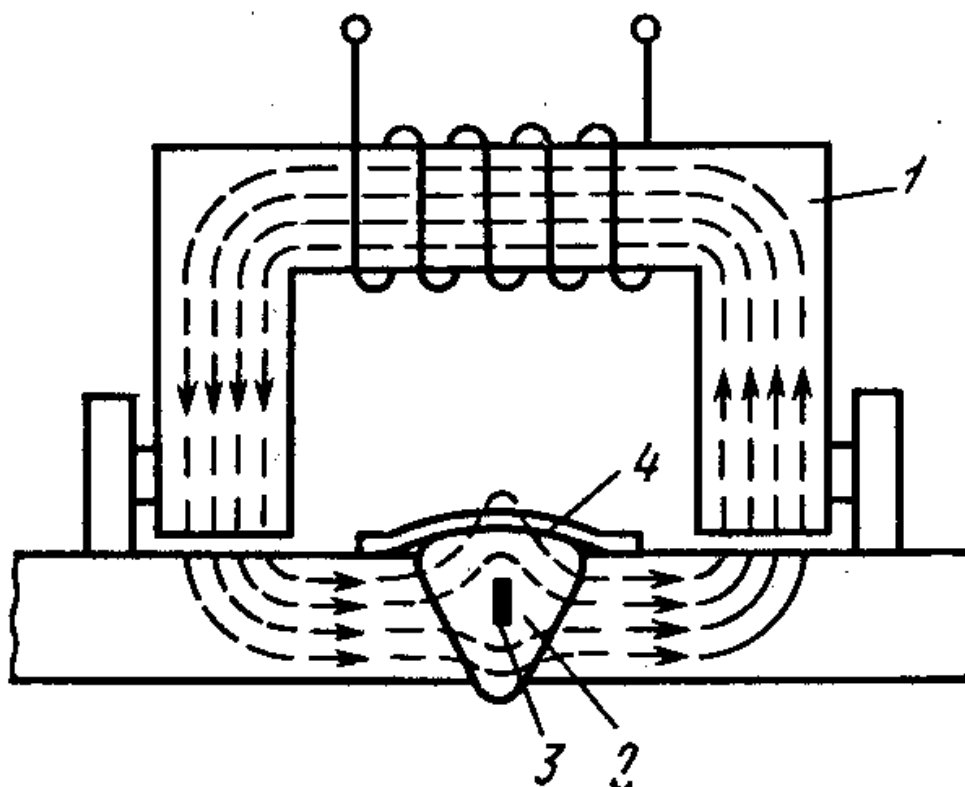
Метод магнитного контроля: 1- магнит; 2 — сварной шов; 3 — дефект; 4 — магнитная пленка
